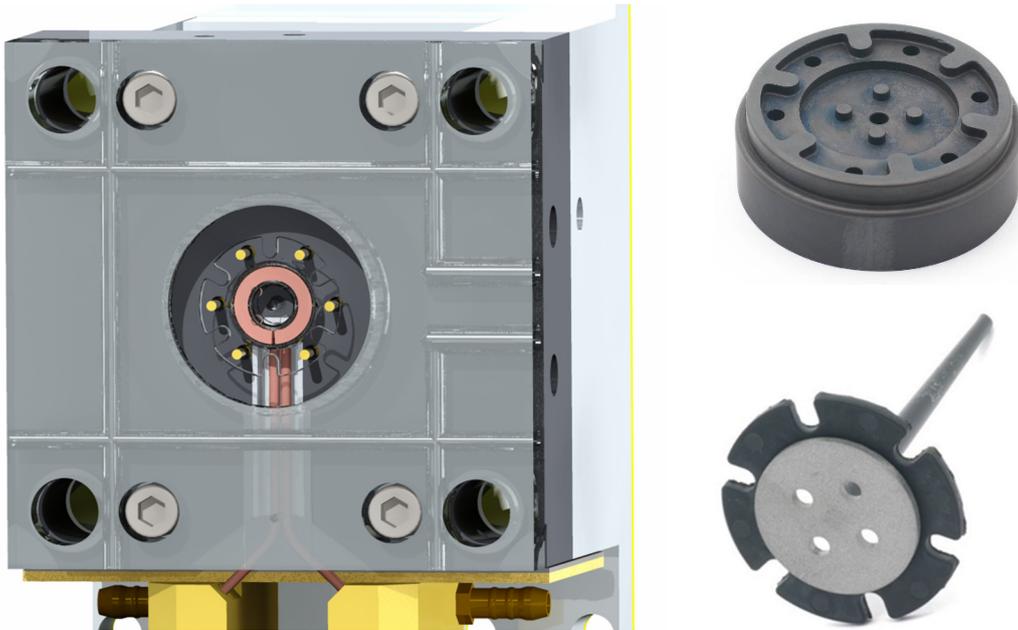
Werkzeug mit voll integriertem Induktor zum Erwärmen von Einlegeteilen aus Stahl, links Werkzeug ohne Formeinsatz mit Blick auf den Induktor, rechts keramischer Formeinsatz und Demonstrator-Bauteil /43/
